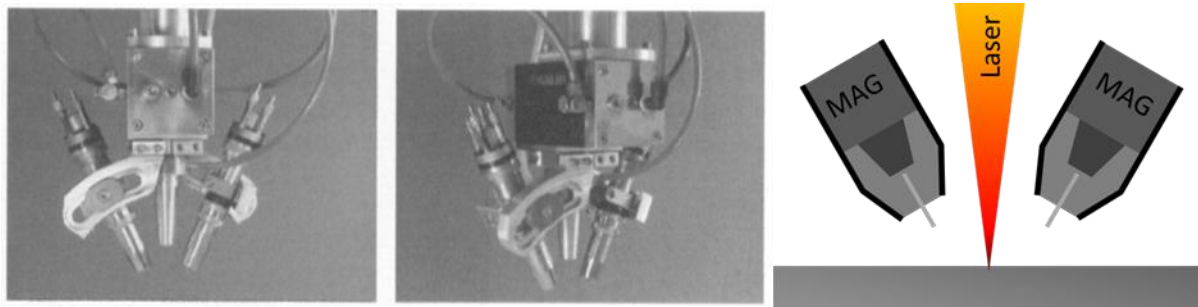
Tête de soudage hybride laser-MAG multicathodes HYDRA [60] et schéma du procédé
